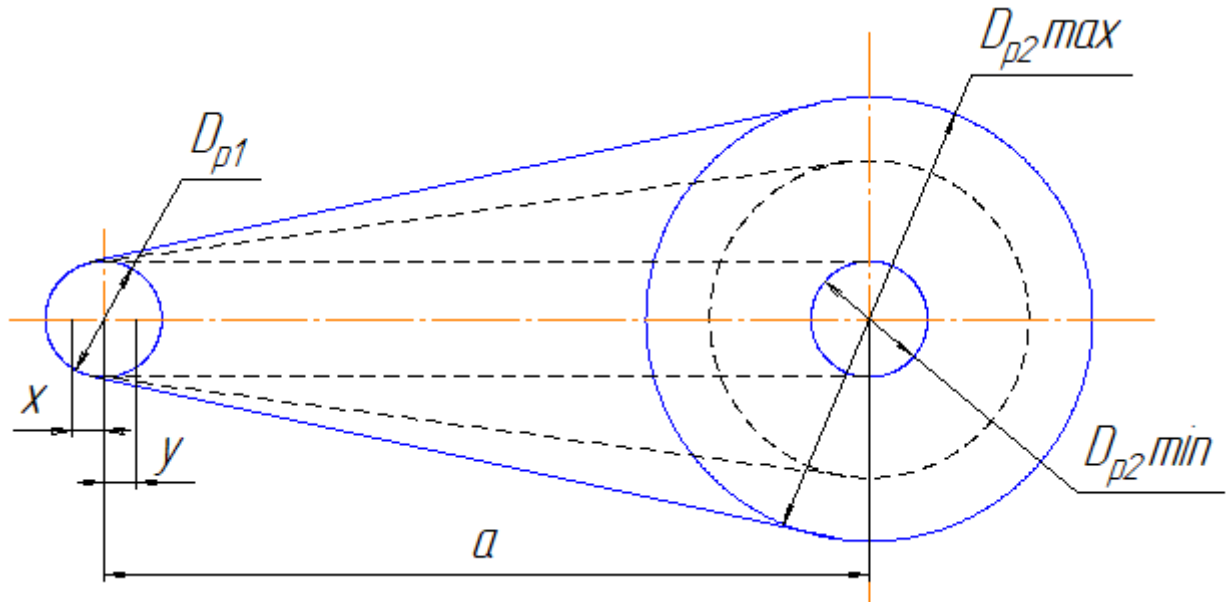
Розрахункова схема варіатора приводного механізму аспіратора
